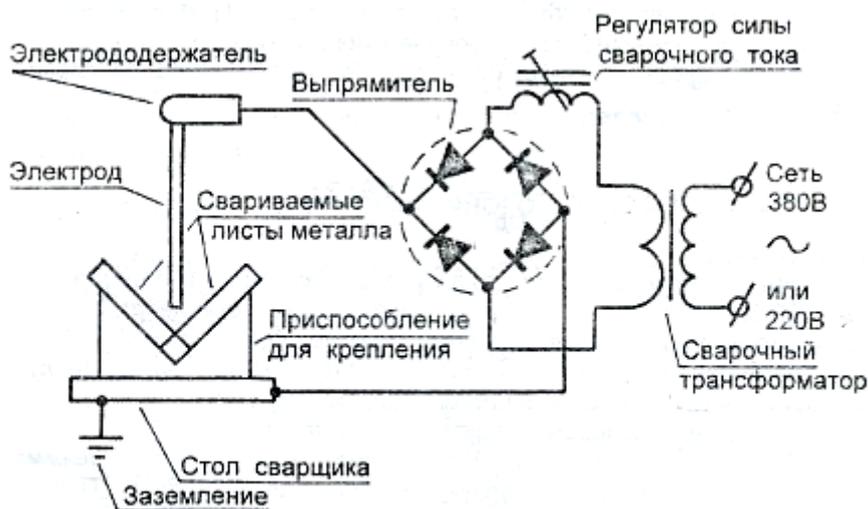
Принципиальная схема сварки выпрямленным током
